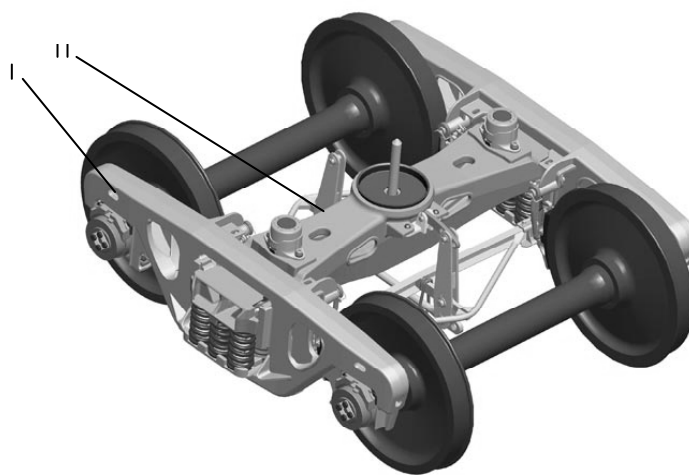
Тележка грузового вагона 18-100 (ЦНИИ-ХЗ): I – рама боковая; II – балка надрессорная
